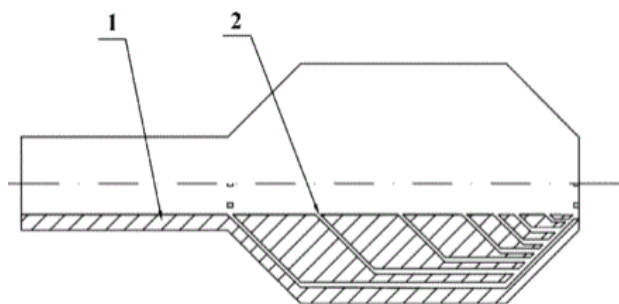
ГЛУШИТЕЛЬ ЗВУКА ВЫСТРЕЛА: 1 – Корпус глушителя; 2 – каналы для вывода пороховых газов
